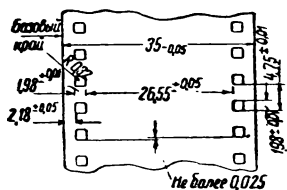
Размеры киноплёнки и перфораций по Норм-кино 43/55
